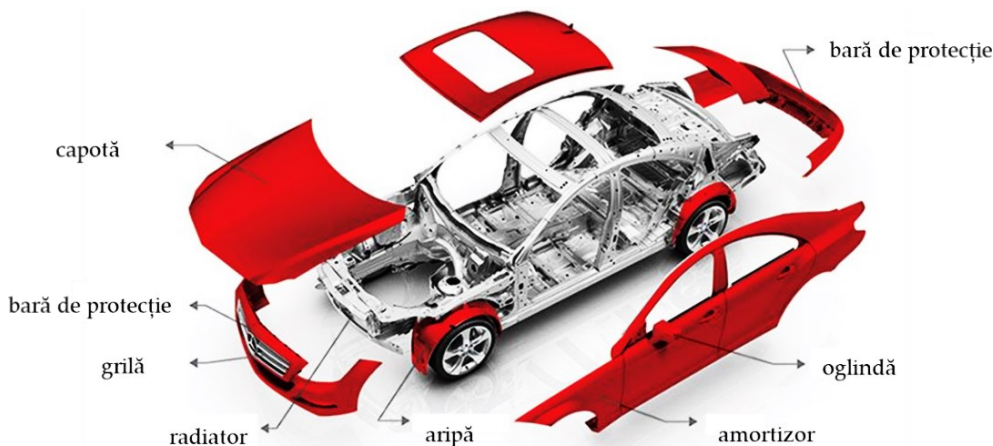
Componente auto obținute din aliaj pe bază de aluminiu [49]
